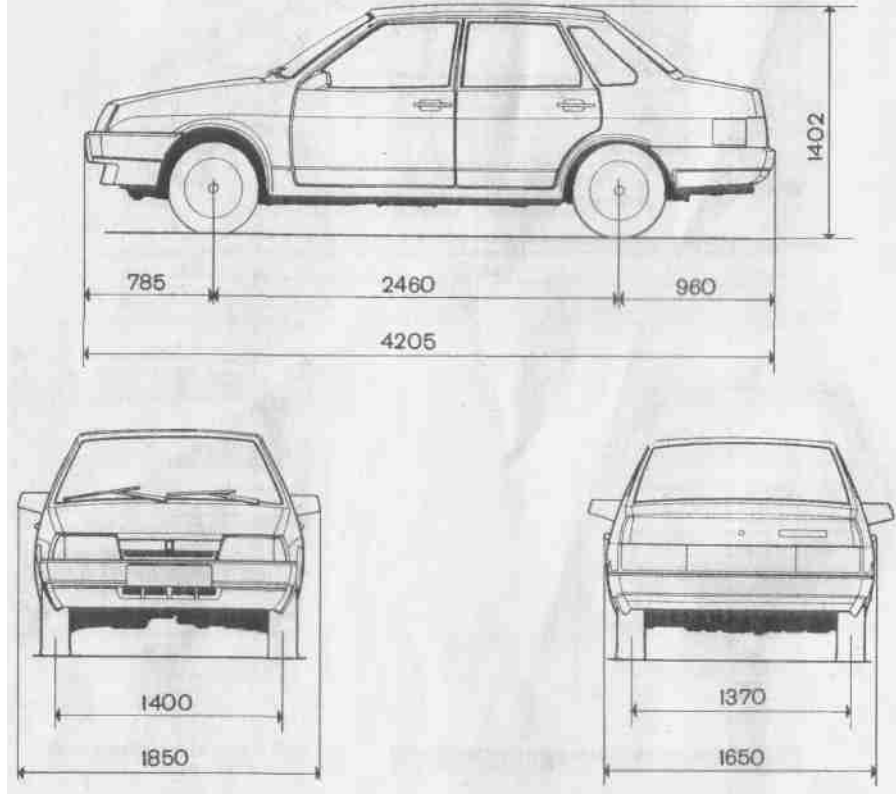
Габаритные размеры автомобиля ВАЗ-21099 и его модификаций
